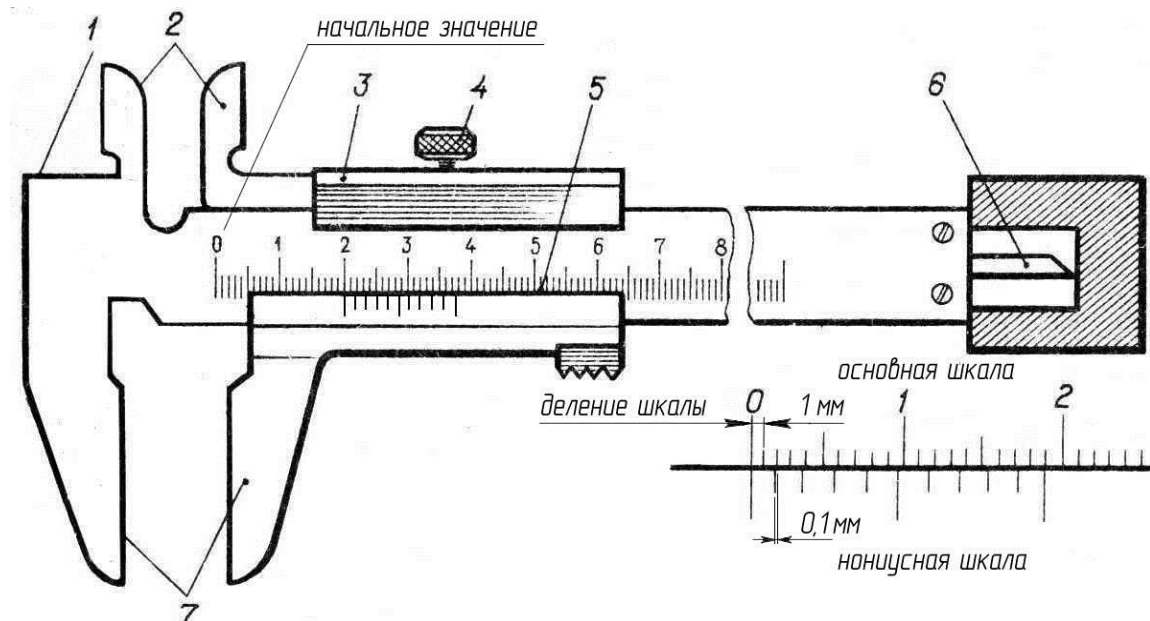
Штангенциркуль ШЦ-I 1 - штанга; 2 – губки для измерения внутренних размеров; 3 - подвижная рамка; 4 - зажим; 5 - шкала нониуса; 6 - линейка глубиномера, 7 – губки для измерения наружных размеров
